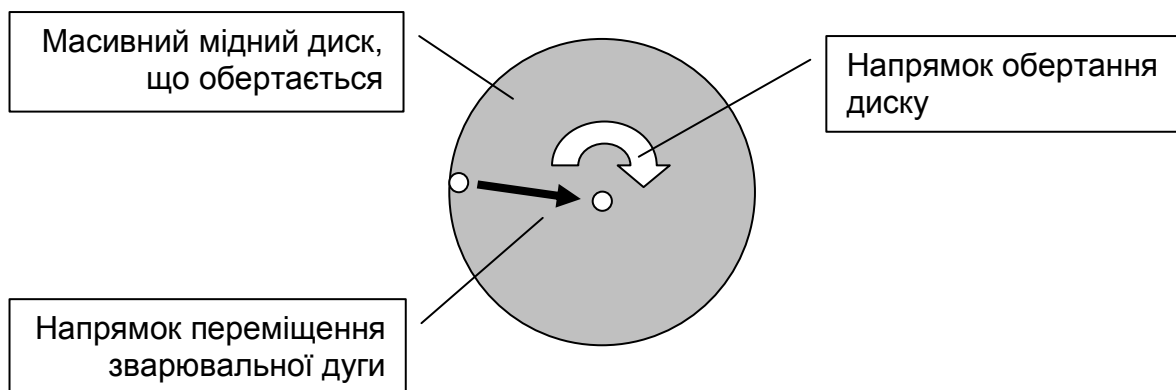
Схема наплавки на масивний мідний диск, що обертається
